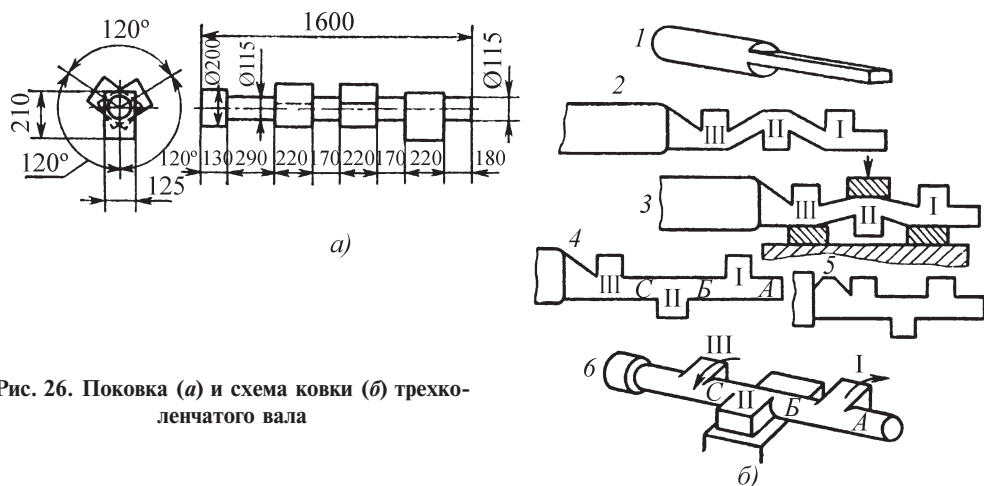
Поковка (а) и схемаковки (б) трехколенчатого вала
